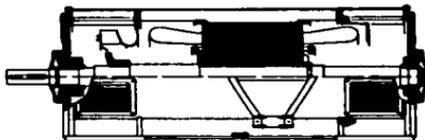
Motor de jaula con cojinetes de rodamientos del ciclo.
